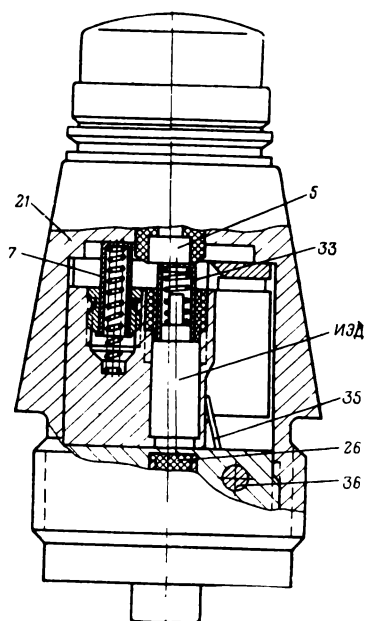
Взрыватель ГПВ-1 (положение деталей после взведения):
